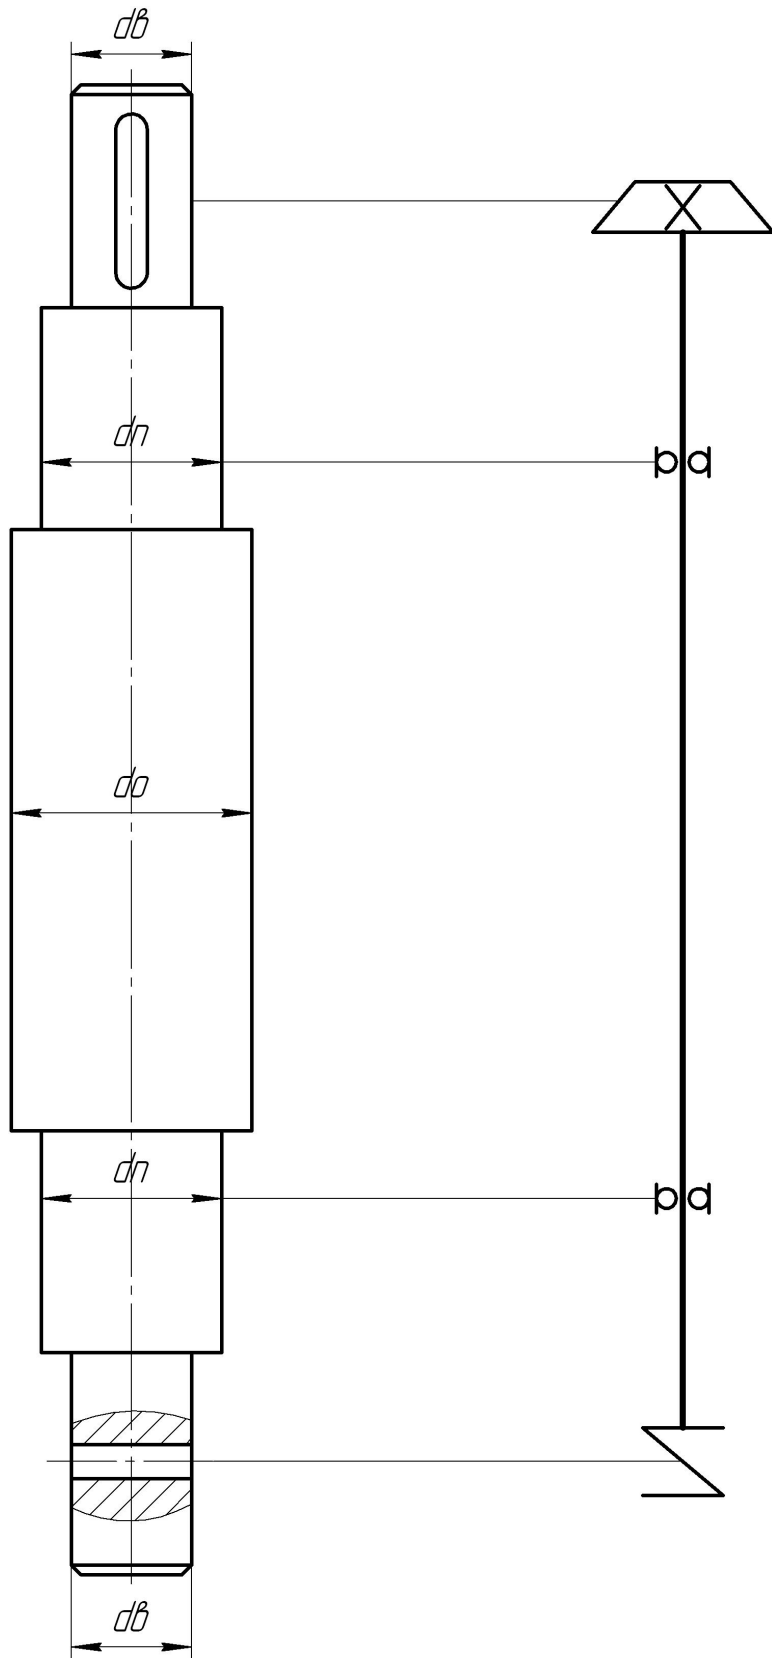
Схема приводного вала подпрессовывающего шнека
